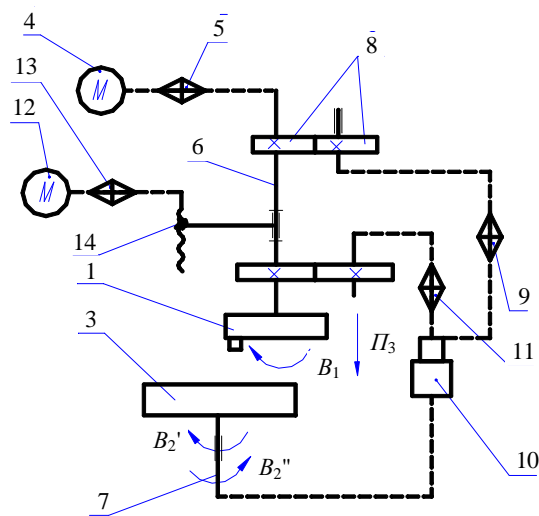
Кинематическая структура станка для обработки ТЗК с переменным отношением угловых скоростей инструмента и заготовки
